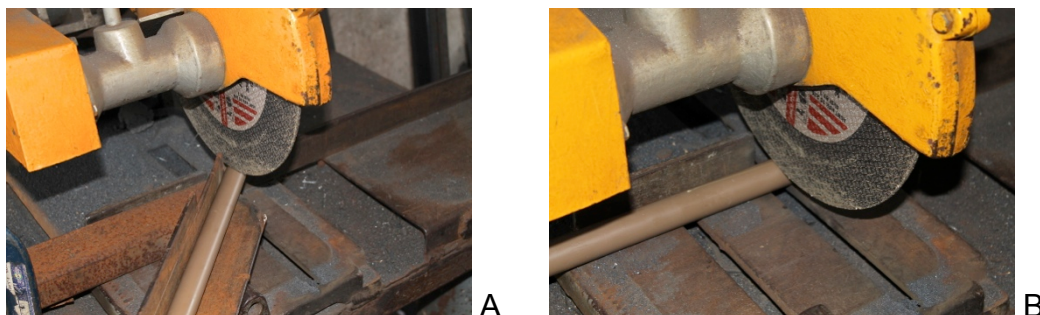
A) tubo de polivinil posicionado sobre esquadro metálico de 30°; B) tubo de polivinil posicionado perpendicularmente à serra policorte para corte.
